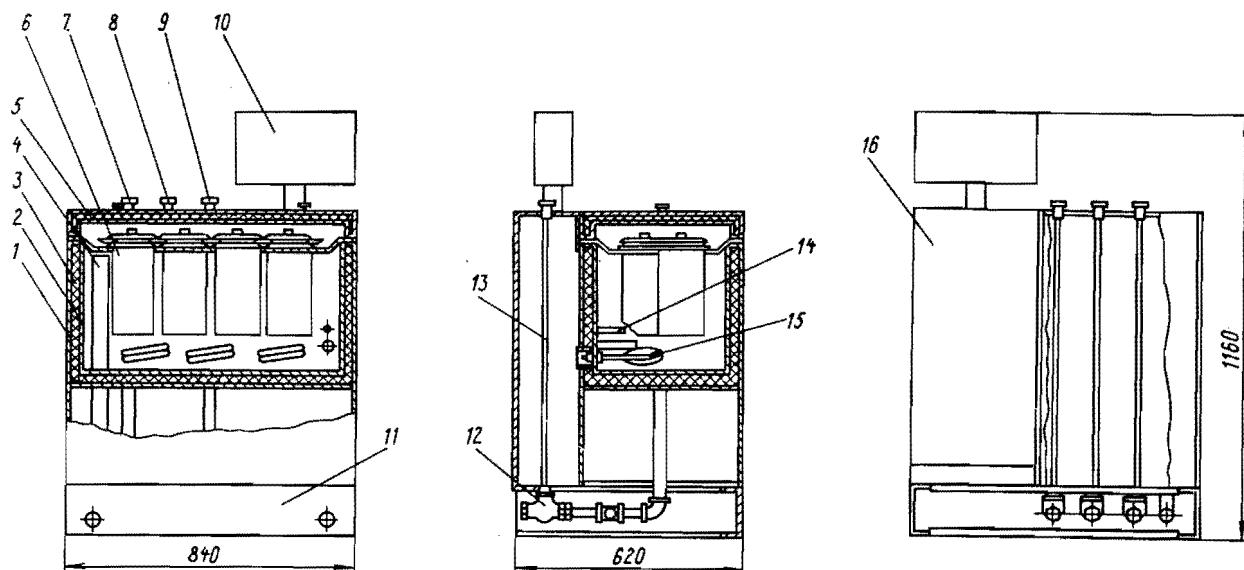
Общий вид заквасочника марки Г6-ОЗ-12:
